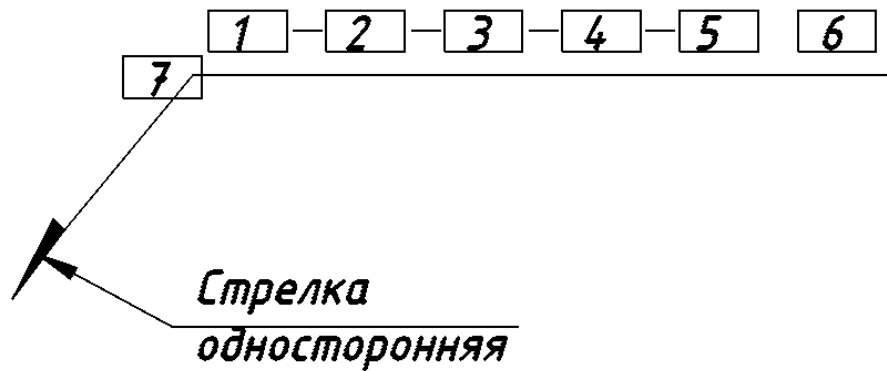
Образец выполнения условного обозначения сварного шва
